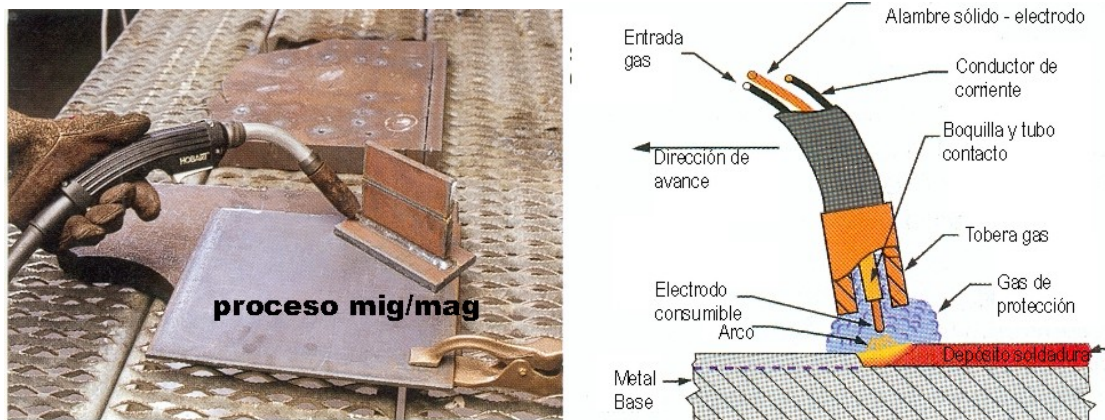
Proceso mig-mag o Gas Metal Arc Welding
